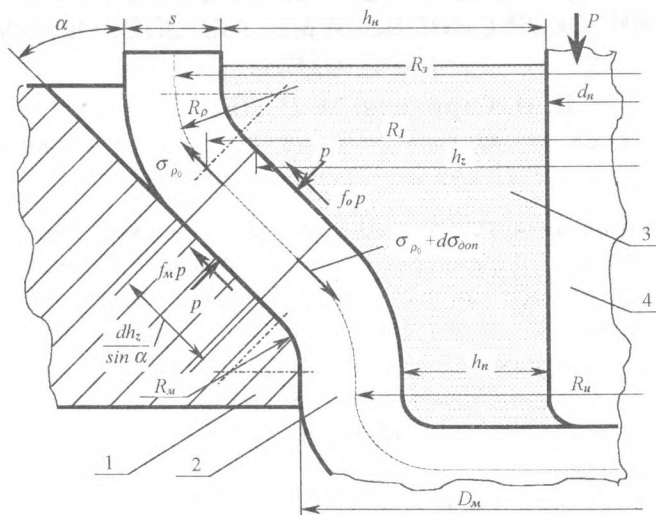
Схема процесса совместной вытяжки покрытия и основы: 1 – матрица; 2 – металлическая основа; 3 – металлопорошковый состав; 4 – пуансон.
